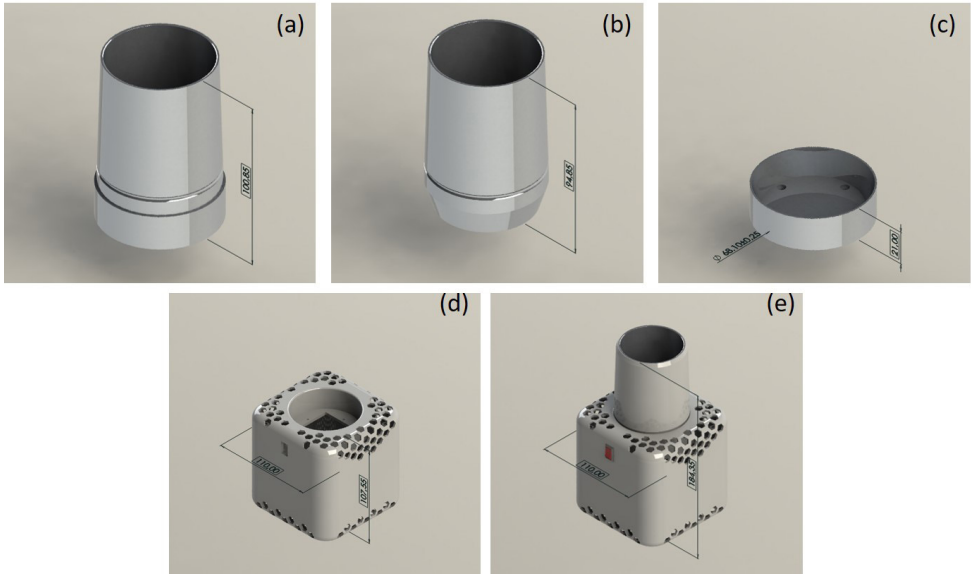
(a) - conjunto de condução em alumínio, (b) - copo em alumínio, (c) - base em alumínio, (d) - carcaça e (e) - conjunto montado, dimensões em mm
